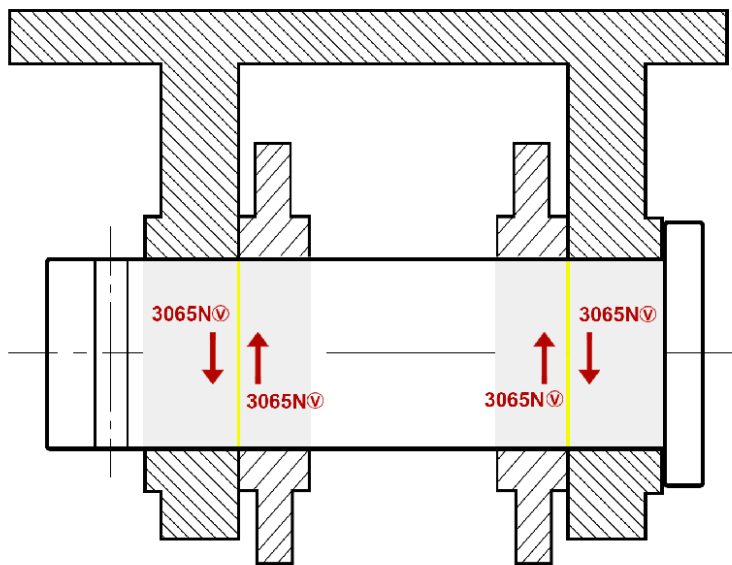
Barra AC-Bancada. SECCIÓN ALZADO
